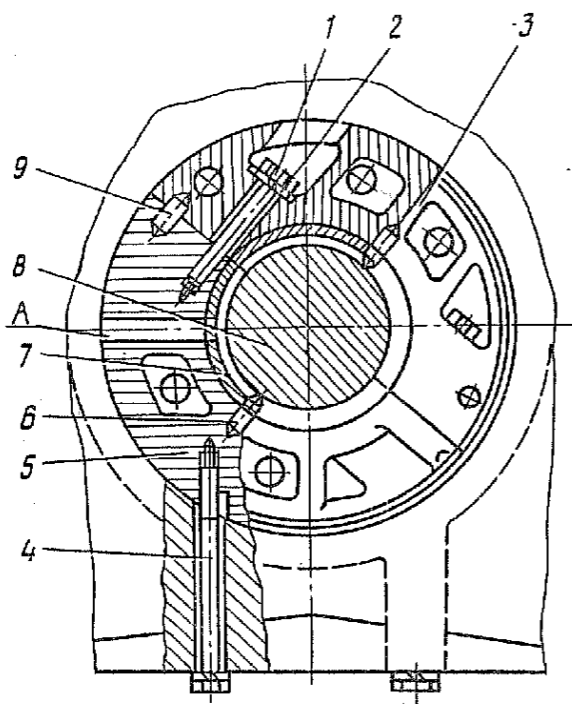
Средняя опора коленчатого вала (вид со стороны носка коленчатого вала):
